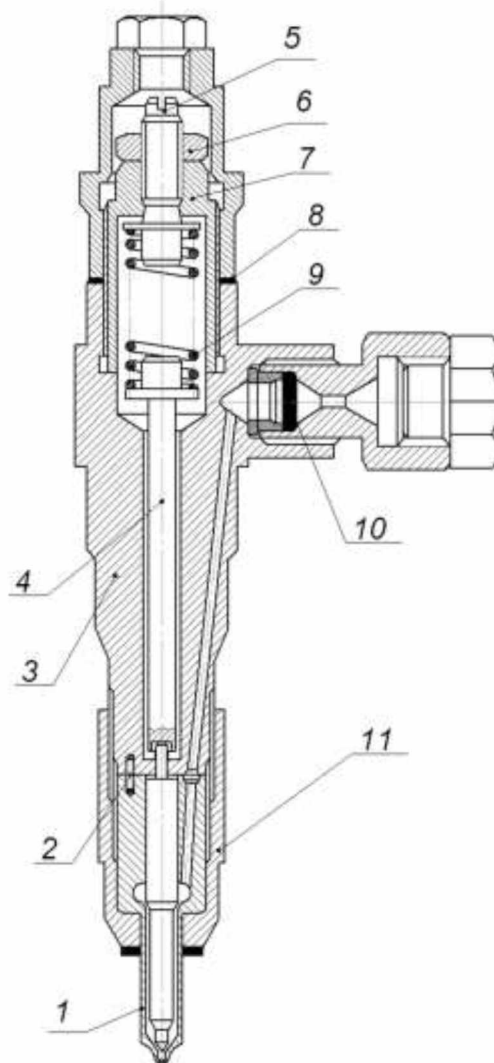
Форсунка з безштифтовим багатоотворним розпилувачем: 1 – розпилувач; 2 – інсталяційний штифт; 3 – корпус форсунки; 4 – штанга; 5 – регулювальний гвинт; 6 – контргайка; 7 – гайка пружини; 8 – прокладки; 9 – пружина; 10 – фільтр; 11 – гайка розпилувача
